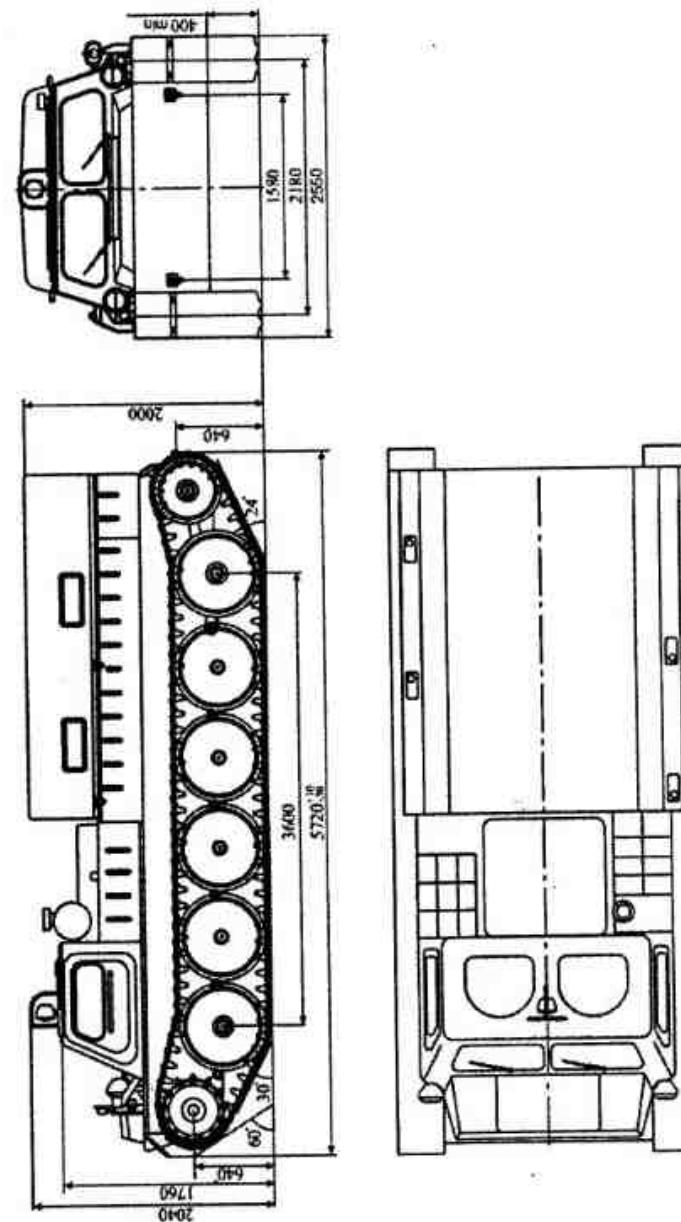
Габаритные размеры снегоболотохода ГАЗ-34039 (34039-00000012/013/022/023)
